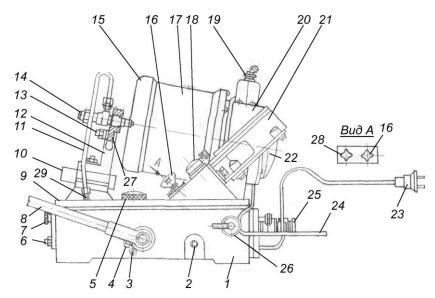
Устройство прибора для испытания и регулировки форсунок КИ-3333
